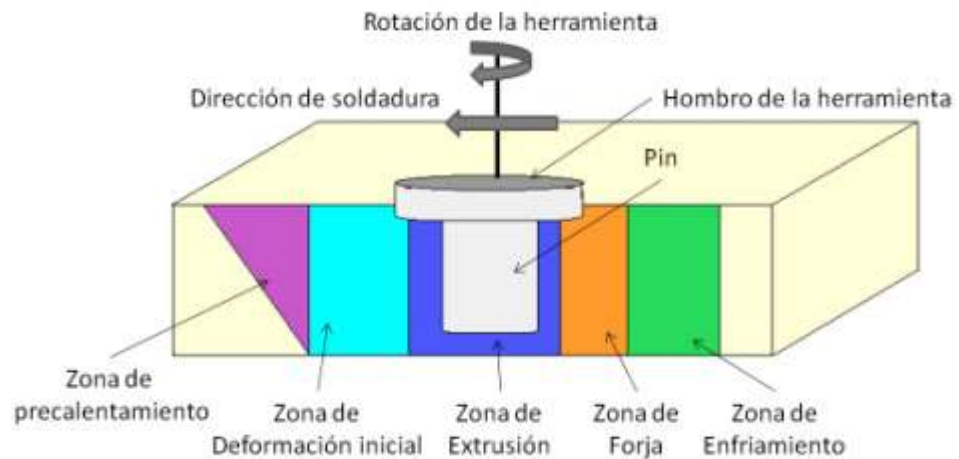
Clasificación de la soldadura por FSW de acuerdo a Arbegast. ⁽⁵⁾
